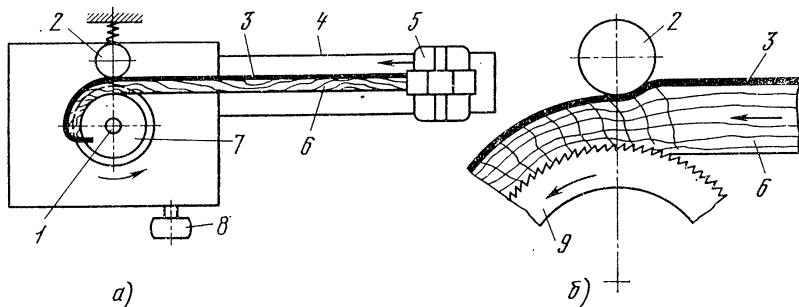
Схема гнутья заготовок в гнутарных станках на замкнутый контур:
